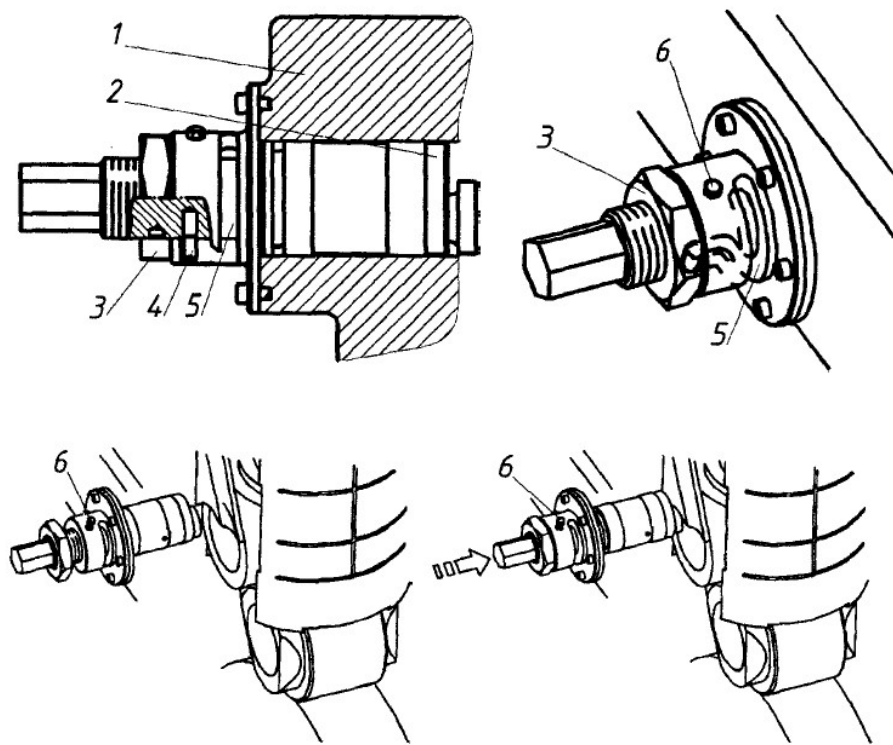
Підйомний і фіксуєчий пристрій штовхача ПНВТ
